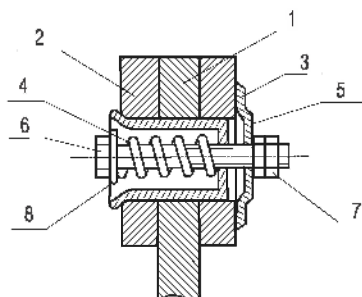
Контакты неразъёмного соединения разъединителей PE19-41, PE19-43
